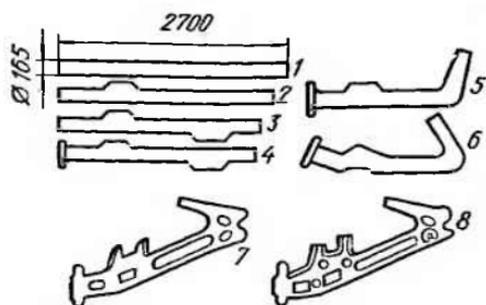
Последовательность (1—8) изготовления сложной поковки из алюминиевого сплава
